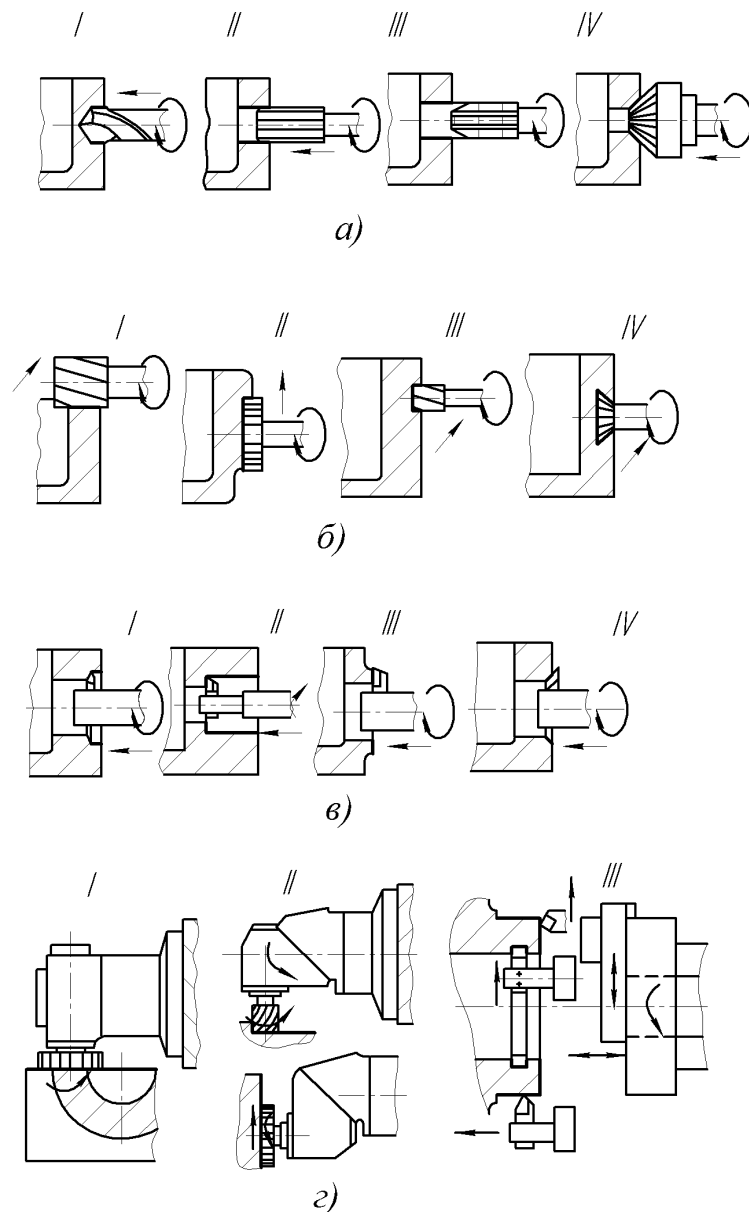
Схеми обробки різних поверхонь на горизонтально-розточувальному верстаті
